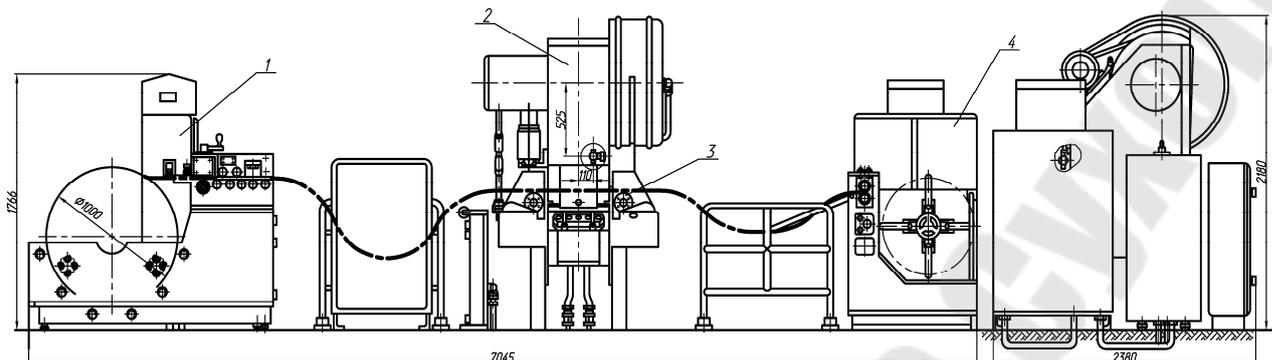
Общий вид автоматического комплекса модели АКД2324В-1: 1 – правильно – разматывающее устройство; 2 – пресс кривошипный КД2324В; 3 – валковая подача ВП38; 4 – наматывающее устройство НУ9
